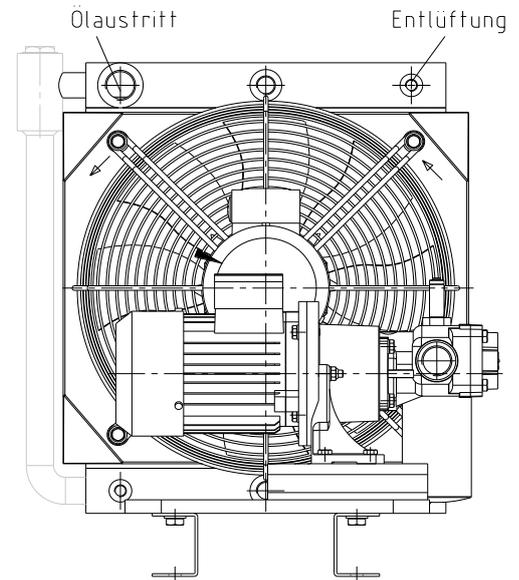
Öl-/Luftkühler; Beispiel: OPC2-300 bis OPC2-900
